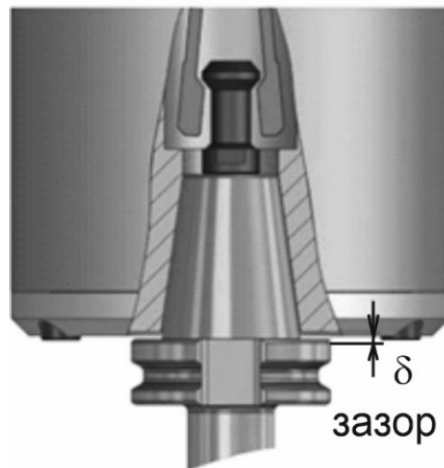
Схема встановлення оправки у шпинделі верстата з базуванням по конусу 7:24
